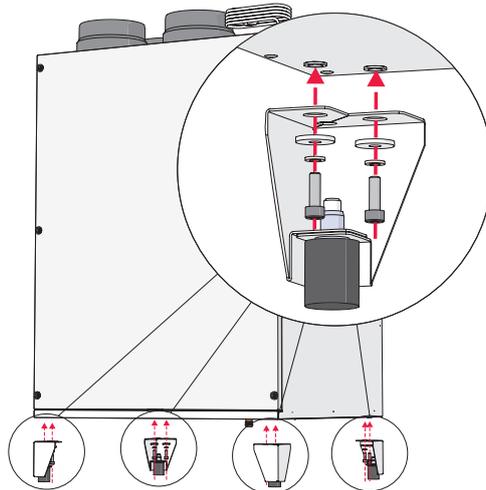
Montaggio a pavimento (accessorio opzionale)
